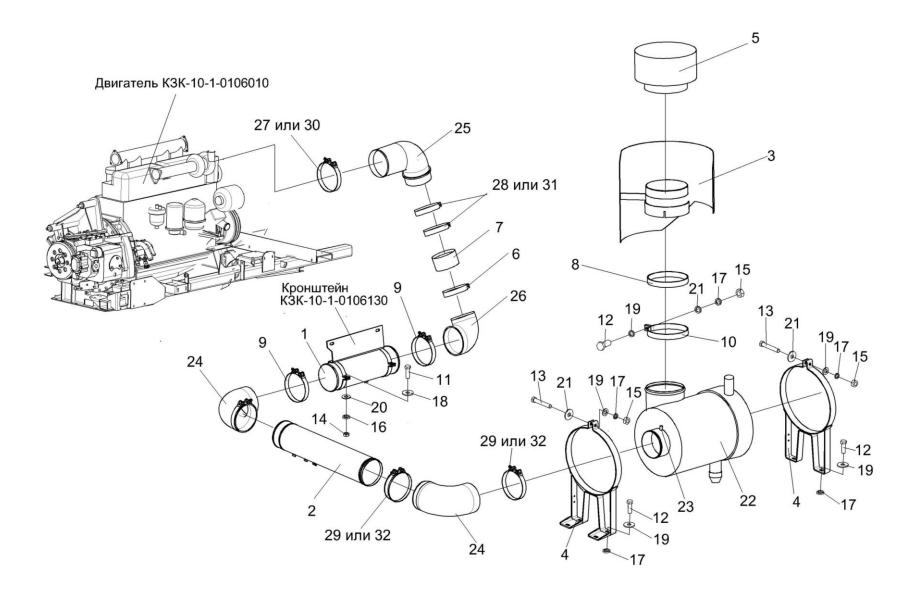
Установка воздухоочистителя КЗК-10-1-0106080
